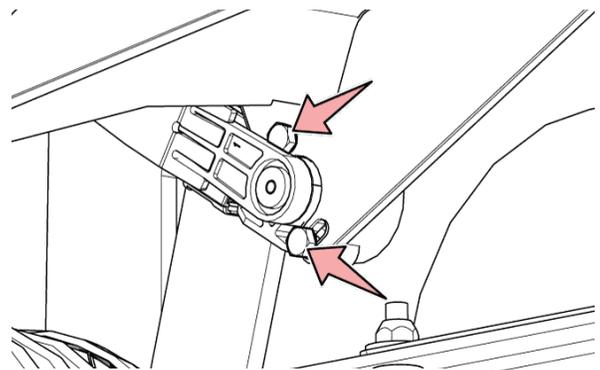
Ajuste del sensor del bastidor auxiliar
